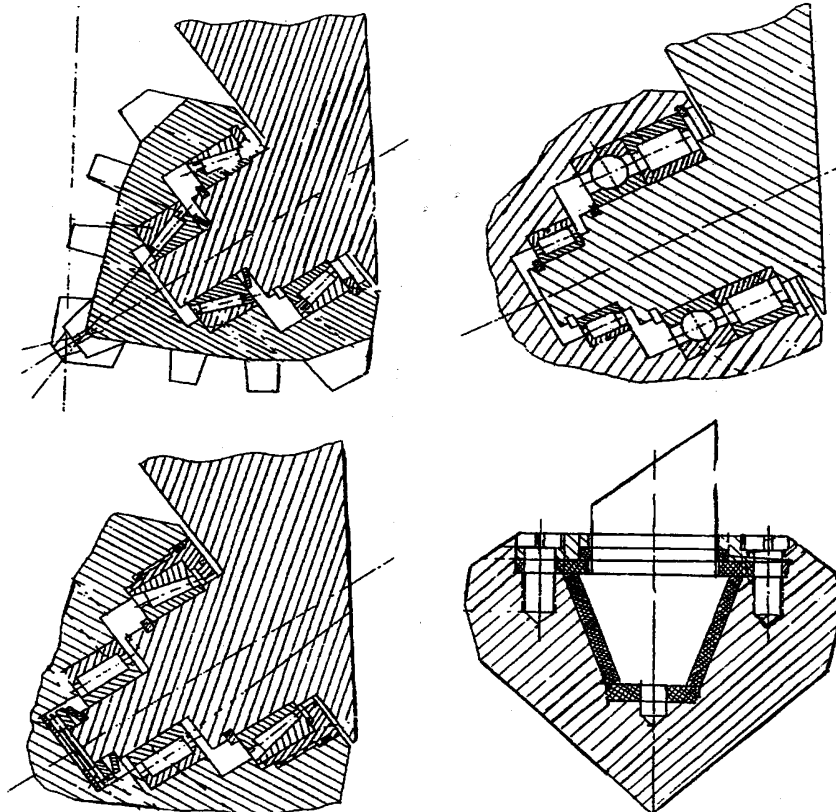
Разновидности опор шарошек с различным расположением подшипников качения
